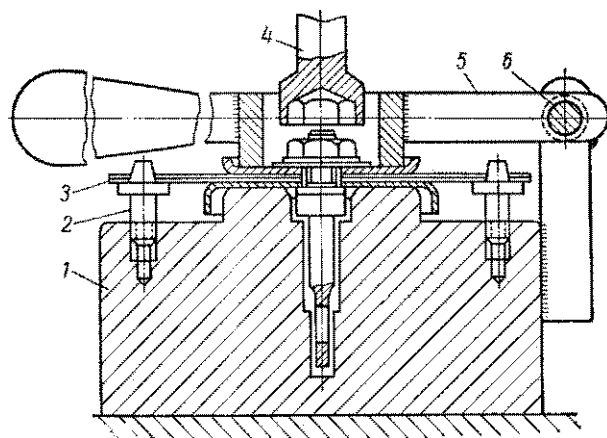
Приспособление для сборки диафрагмы топливного насоса:
